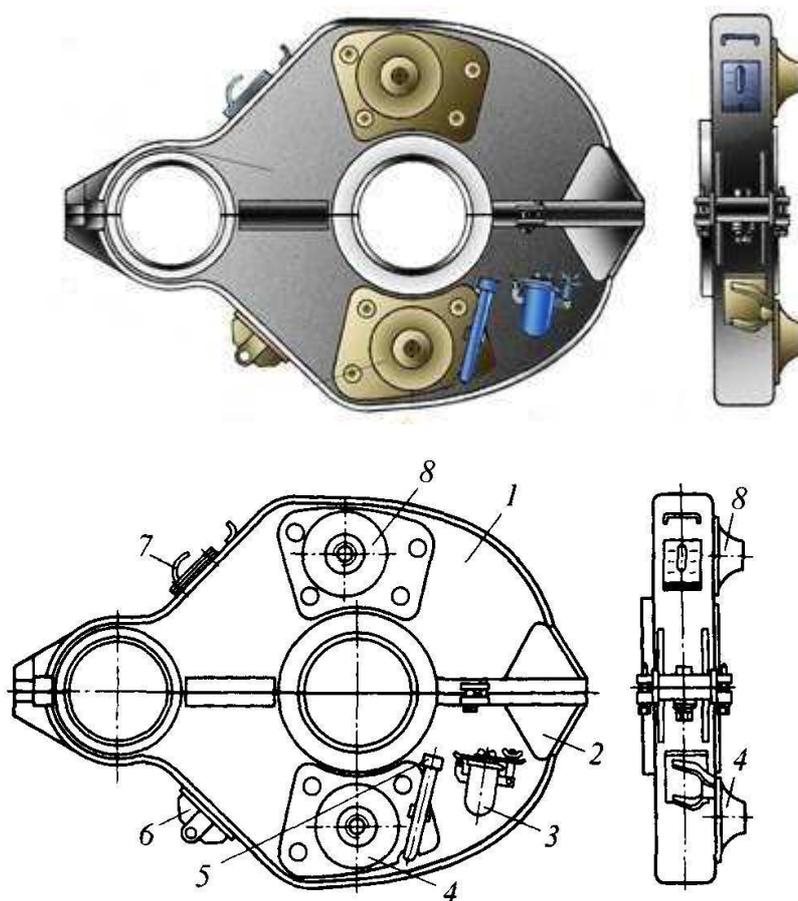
Кожух зубчатой передачи: 1,2 — верхняя и нижняя половины кожуха; 3 — масленка; 4,8 — бобышки; 5 — указатель уровня масла; 6 — кронштейн; 7 — сапун
